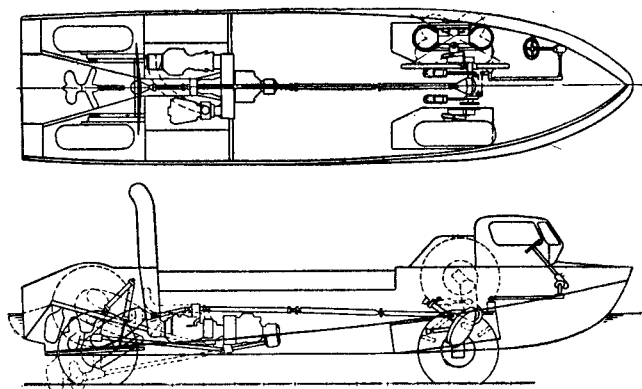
Схема расположения агрегатов плавающего автомобиля «Сихорс II»
